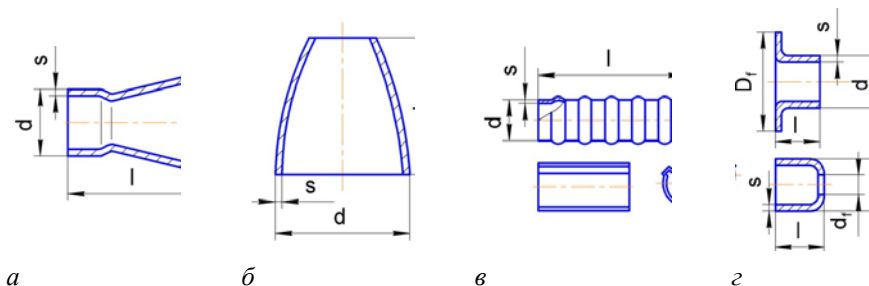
Типовые операции магнитно-импульсной формовки трубчатых заготовок
